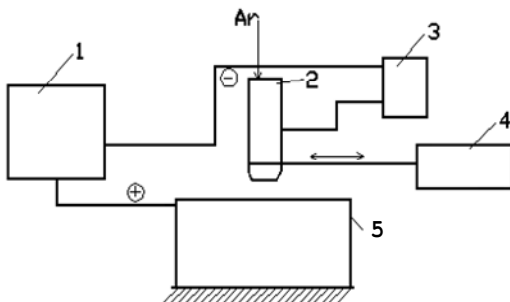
Принципиальная схема установки для поверхностной плазменной закалки:
